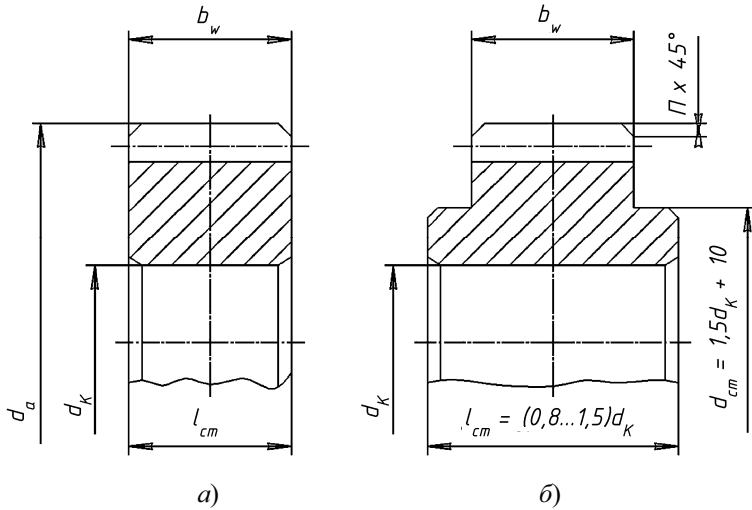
Цилиндрические зубчатые кованные колеса при $d_a < 150$ мм:
